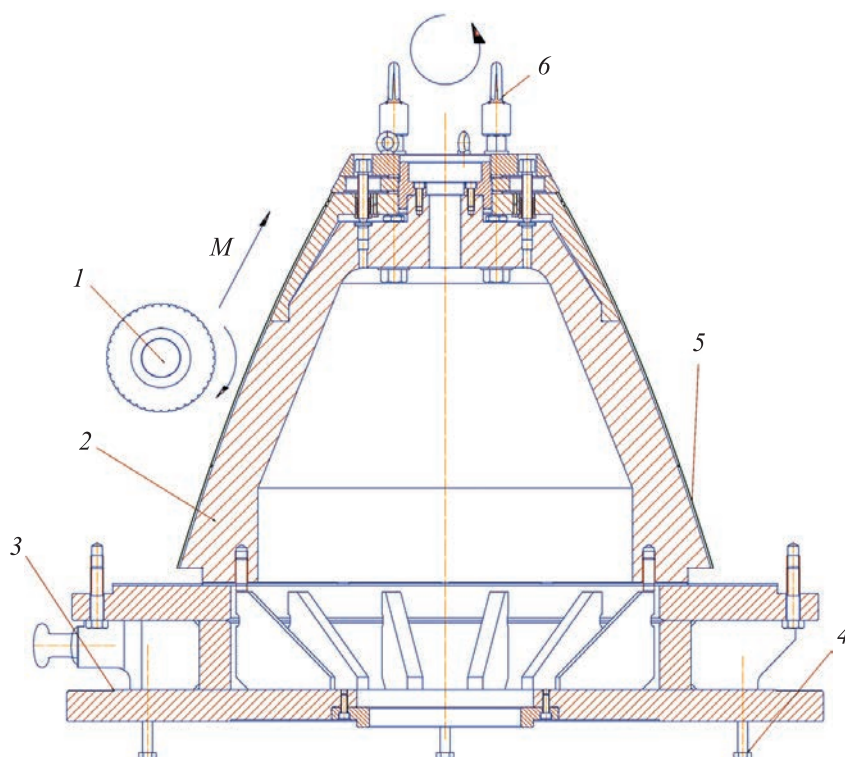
Схема технологического приспособления и схема обработки при формировании искусственной шероховатости на поверхности детали:
